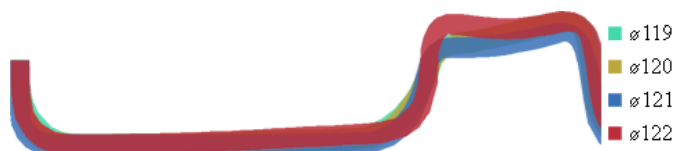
Геометрия тыльной стойки и замковой впадины опалубочного профиля
